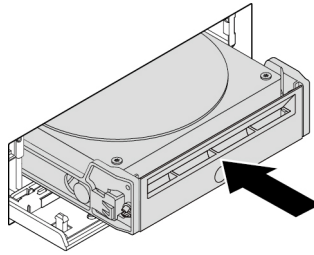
Installation de l'unité de stockage 3,5 pouces dans le boîtier de stockage d'accès frontal
